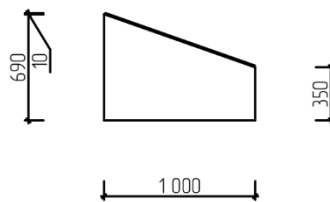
Чертеж оборудования. Вид сбоку
